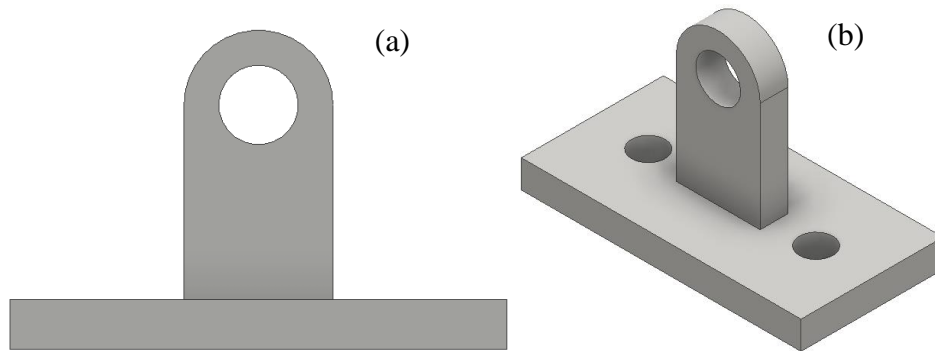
Soporte de unión actuador lineal giro asiento/asiento Vista Frontal (a) Isometrica (b)
